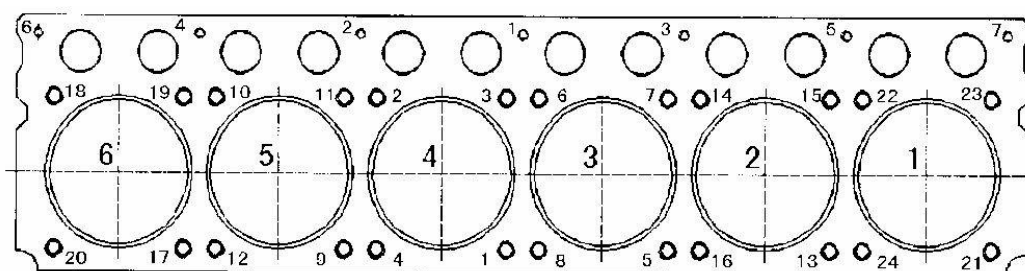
Последовательность затяжения главного болта и вспомогательной гайки головки цилиндра
